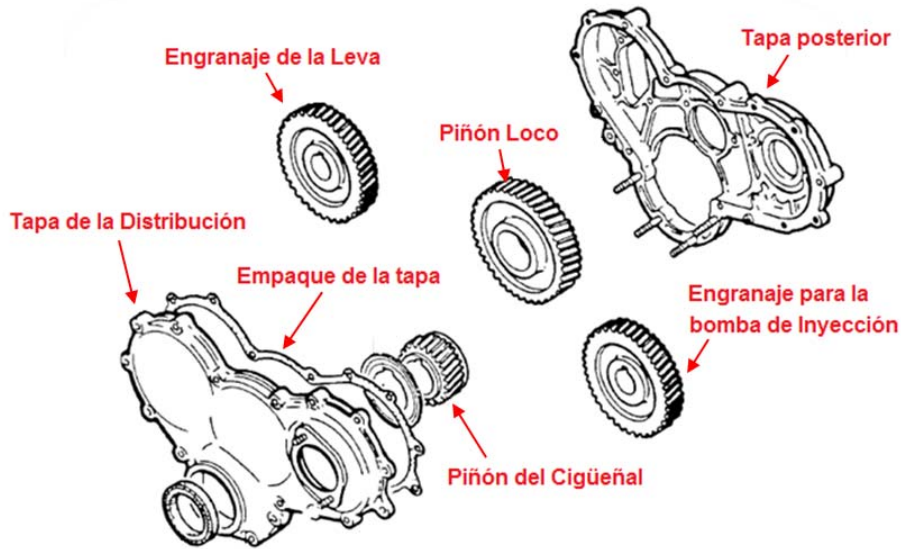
14 Engranajes de la distribución del Motor Kia Asia Hi-Topic.
